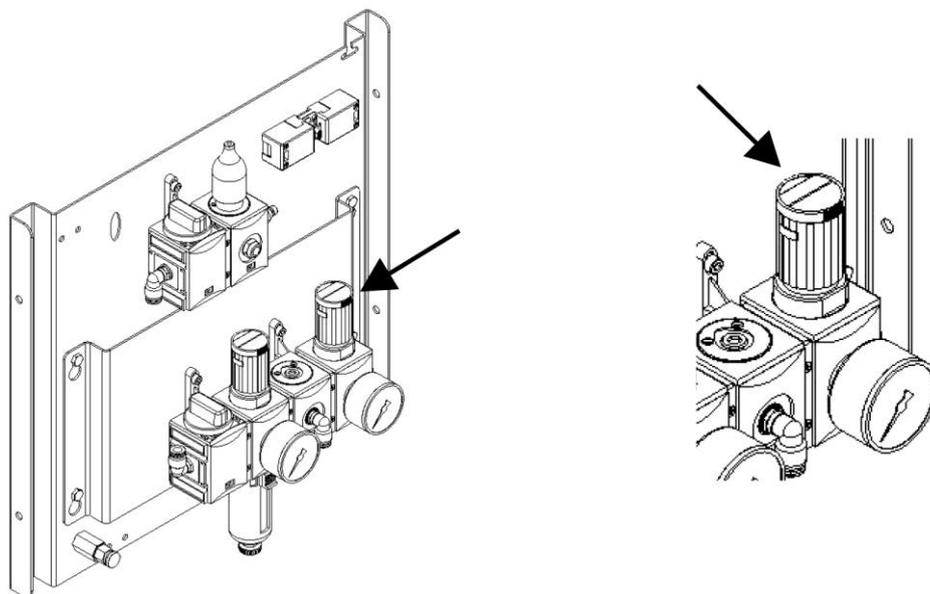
réglage de la pression du dispositif de levage / bac collecteur de poussières
